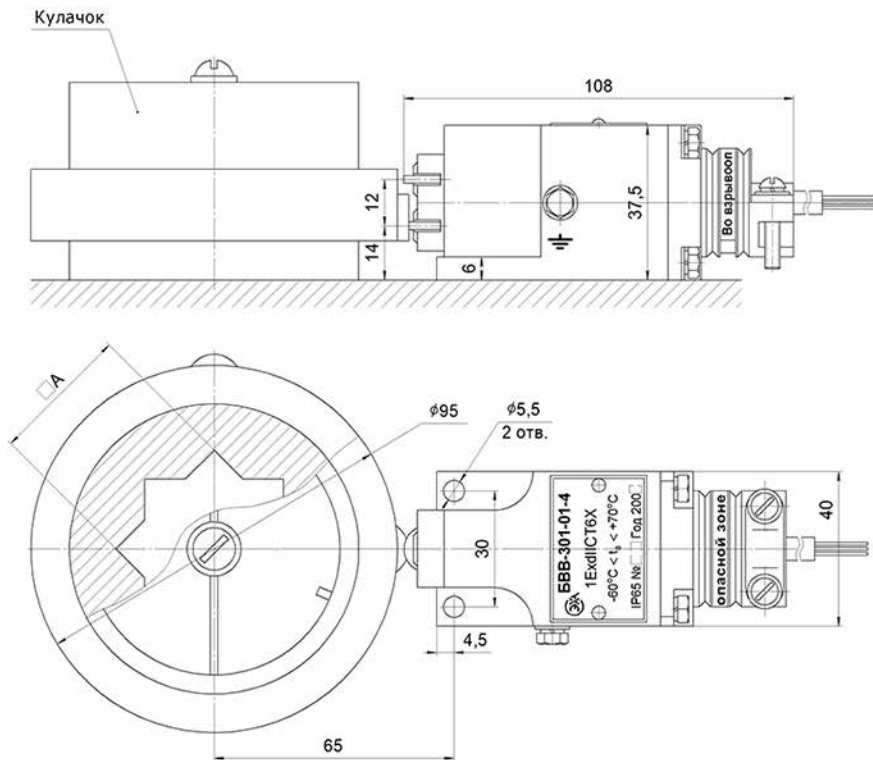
Габаритные и установочные размеры блока выключателей БВВ-301-01
